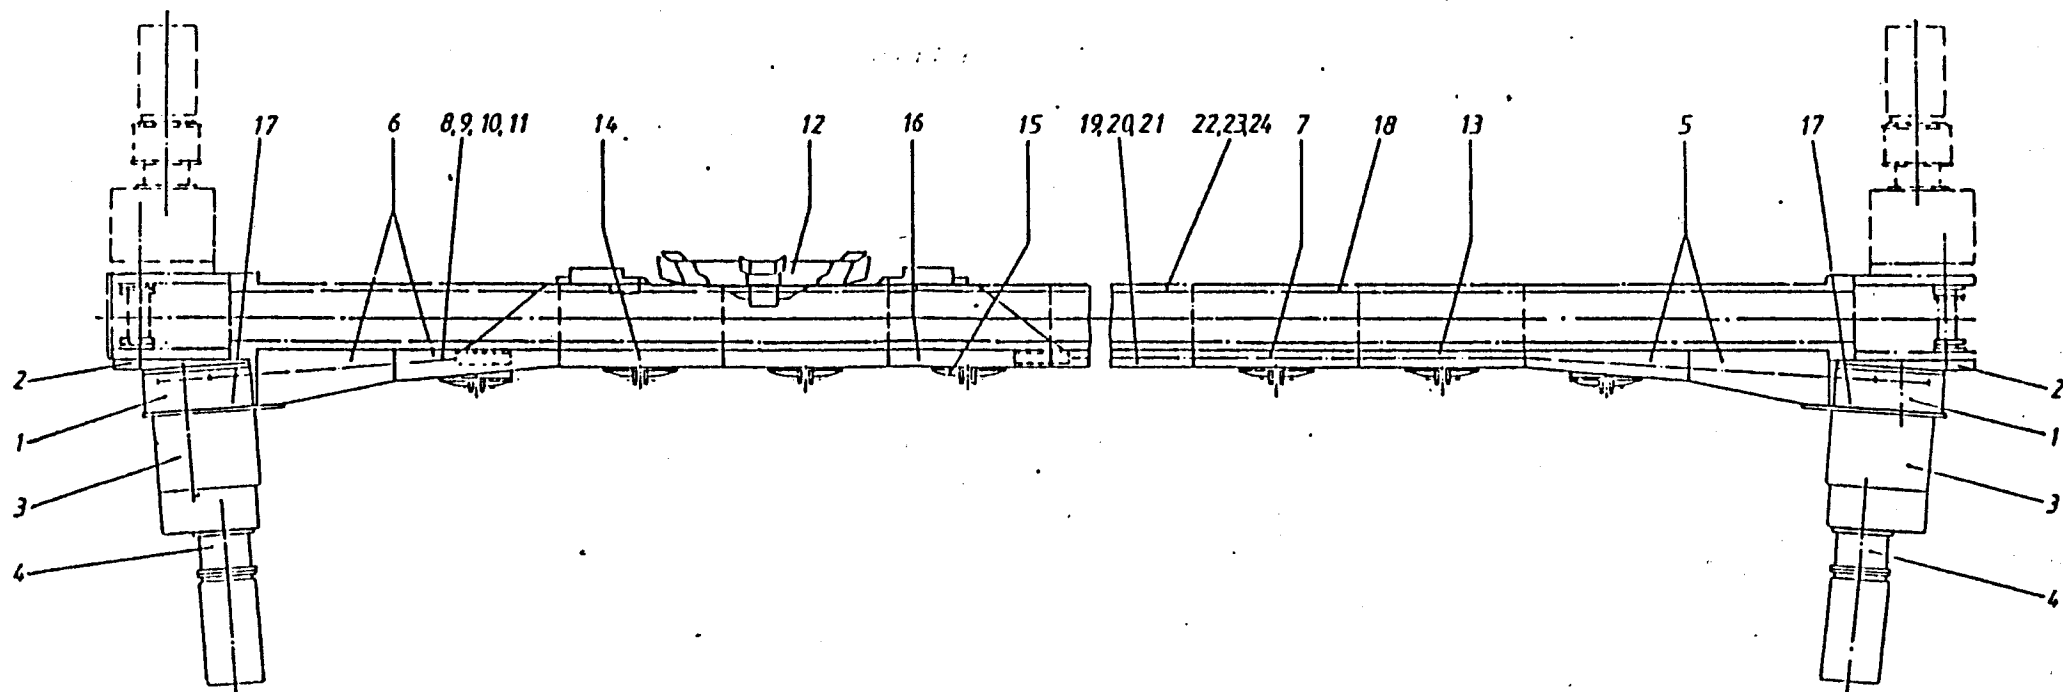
CONJUNTO CEPILLO SH9-SK SOBRE TRANSPORTADOR BLINDADO UFV 26/500
